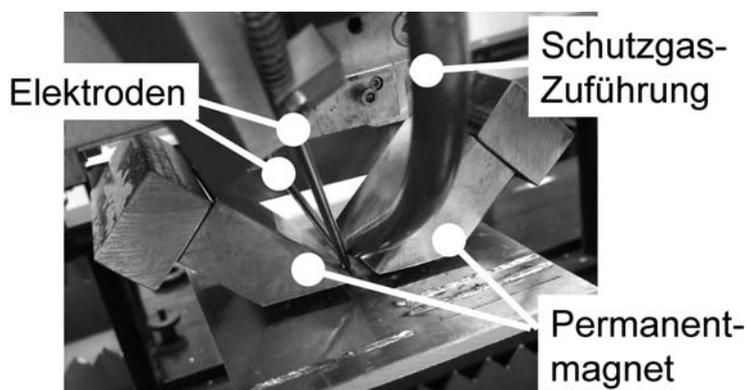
Konvektives Magnetsystem integriert in eine Laserbearbeitungsanlage. Die Permanentmagnete und die Elektroden wurden an einem Spiegelbearbeitungskopf für das Schweißen mit CO₂Lasern befestigt.
